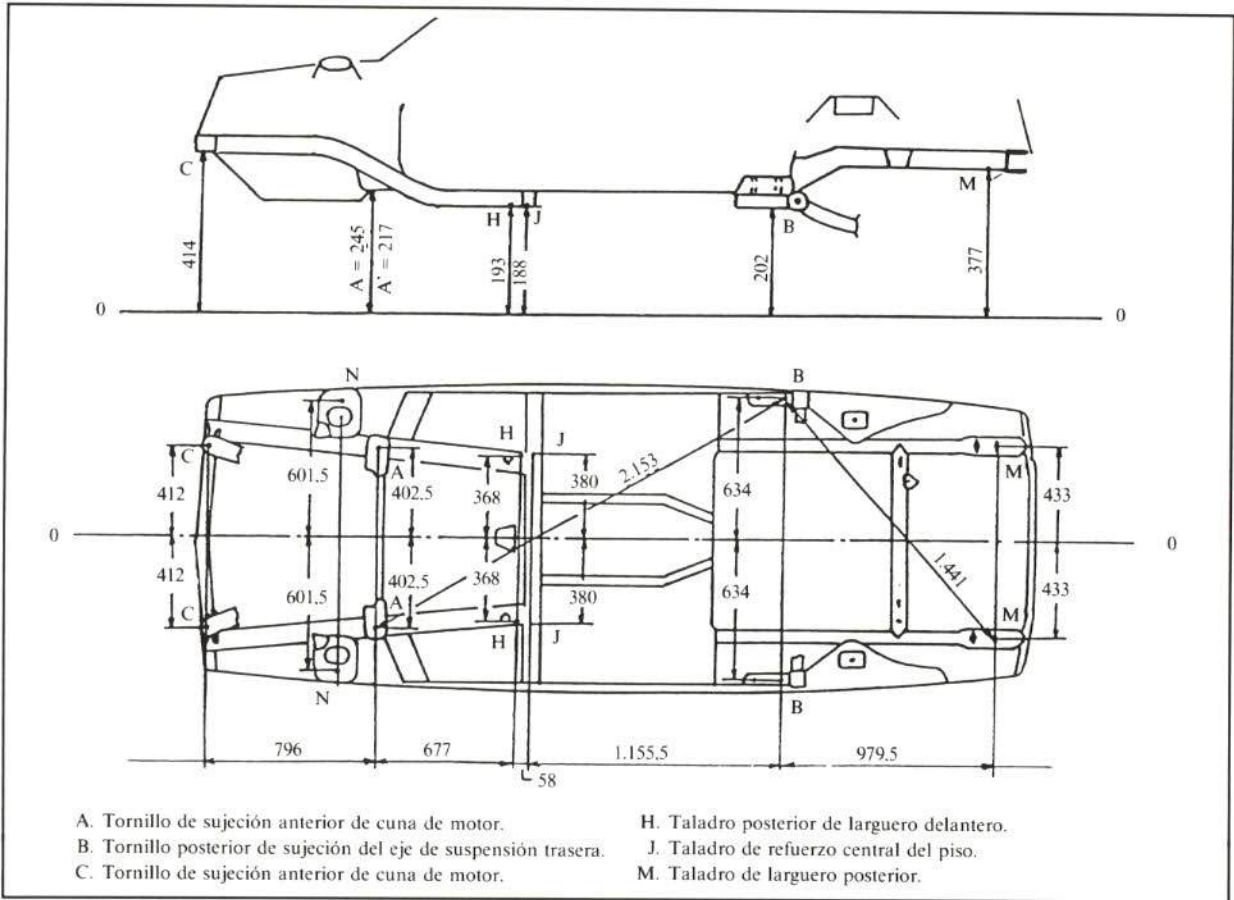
Dimensiones del vehículo en planta y alzado.
